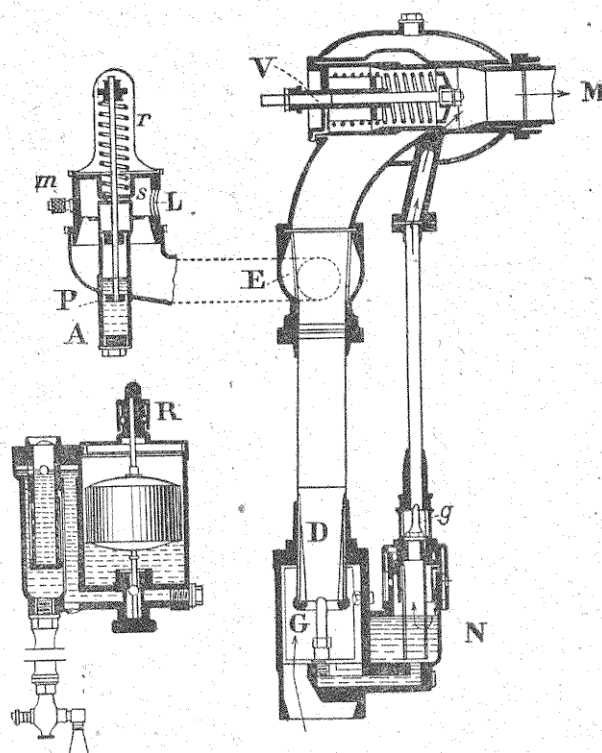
Coupe du carburateur Delaunay-Belleville.
